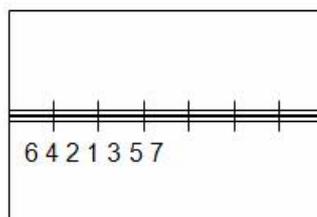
Обратнo-ступенчатая сварка
